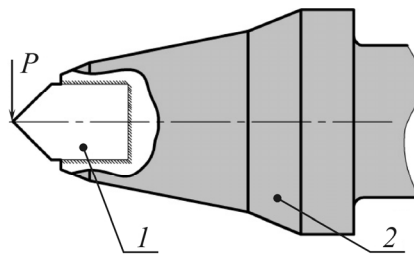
Расчетная схема для определения эквивалентных напряжений в твердосплавной вставке цилиндрической формы:  $P$  — изгибающая сила; 1 — твердосплавная вставка; 2 — корпус тангенциального поворотного резца
